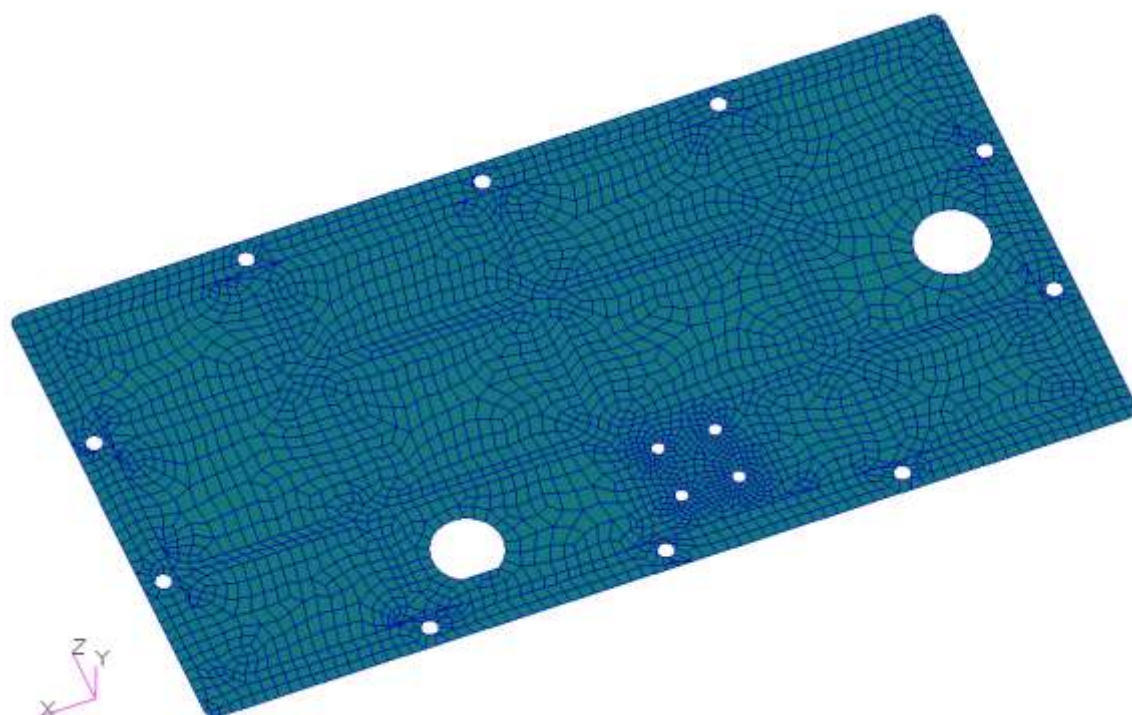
Parete inferiore dell'EEB (*Bottom Wall*)
